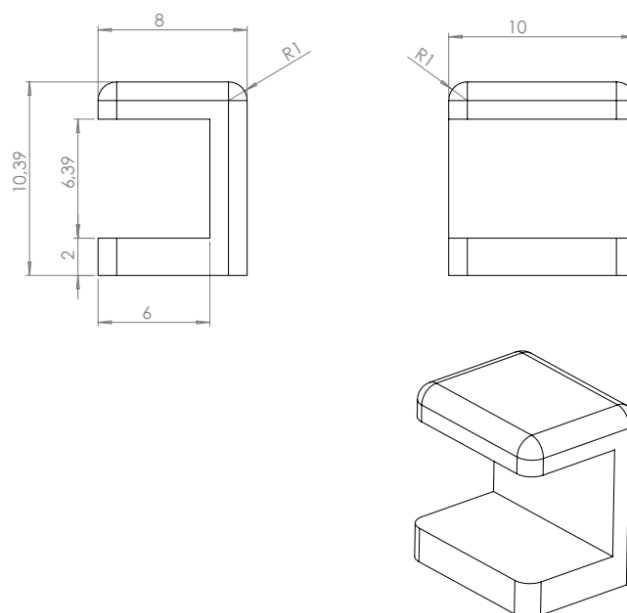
Desenho técnico do fixador criado. As dimensões estão em milímetros.
